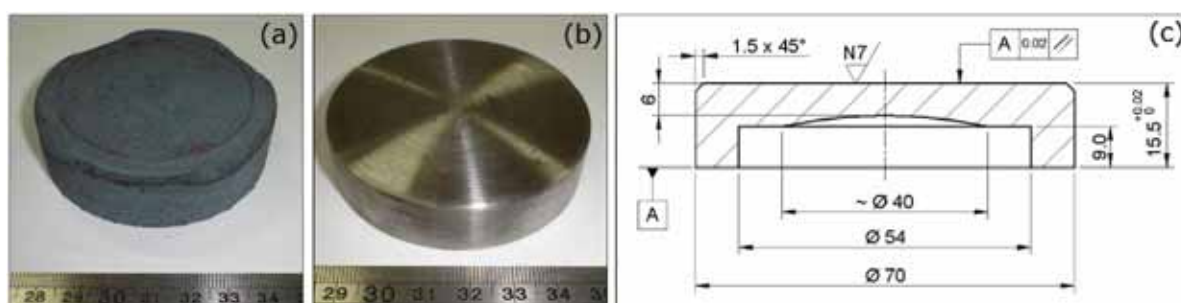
(a) vista superior em perspectiva da amostra bruta, (b) vista superior em perspectiva da amostra pré-usinada e (c) desenho técnico para os ensaios finais de fresamento dos corpos-de-prova.
